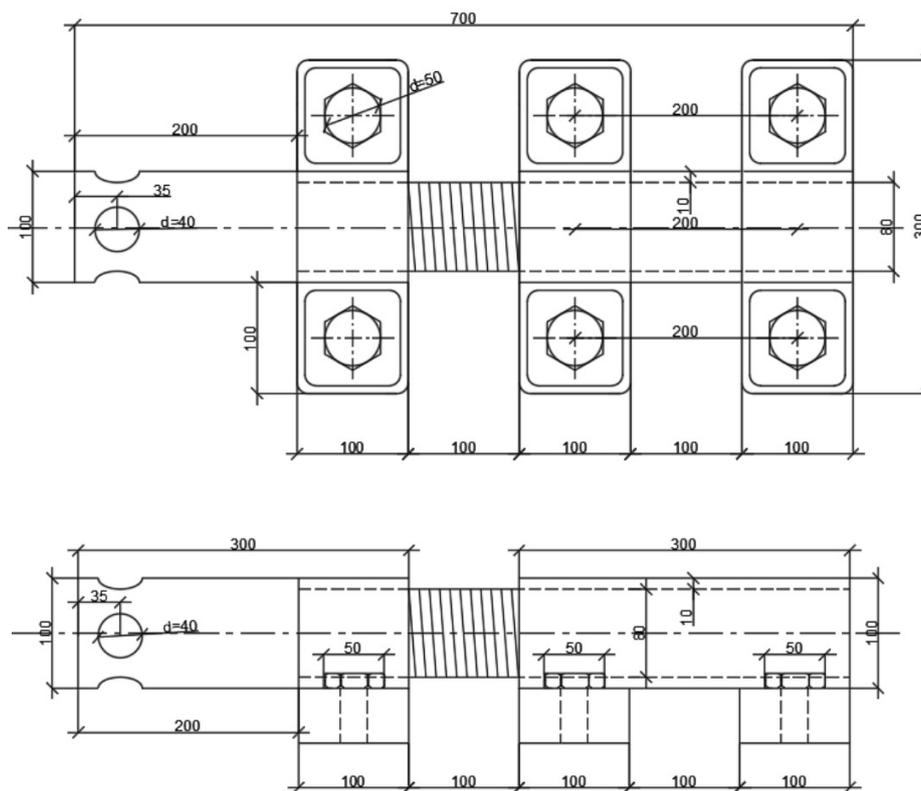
Общий вид проектируемой металлической формы для свай с ребристой боковой поверхностью: А) двухместная форма для ребристых свай; Б) Разрез формы, ребра опалубки из прокатной стали; В) Вид сверху крышки формы
